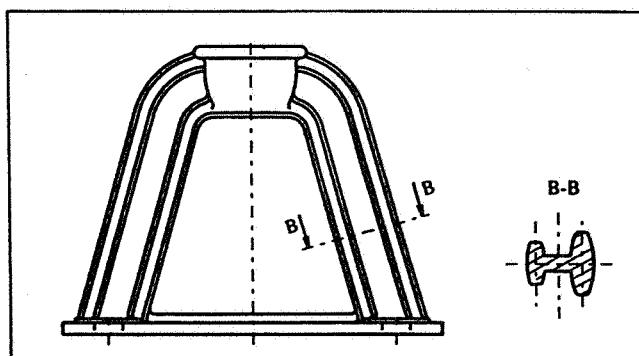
Se la sezione è posta in posizione diversa da quella della figura
